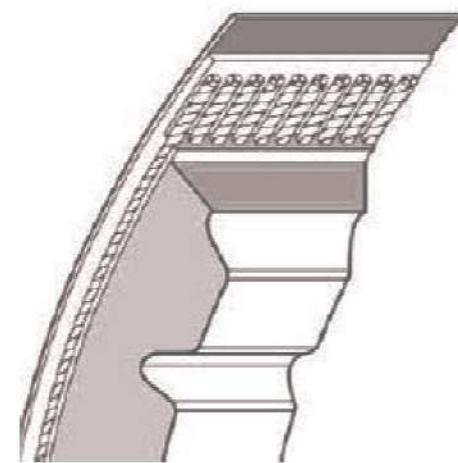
Клиновой узкий ремень с зубчатой кромкой без обертки боковых граней
